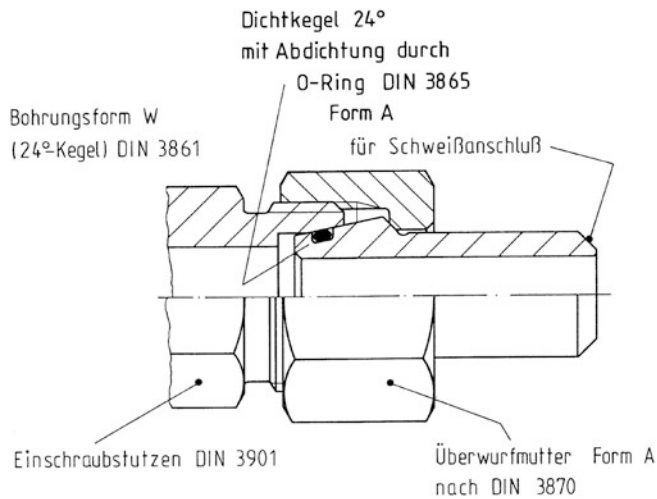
Dichtkegelverschraubung 24° mit O-Ring (DIN EN ISO 8434-4, Schweißkegel-Verschraubung SKA, Parker-Ermeto)
